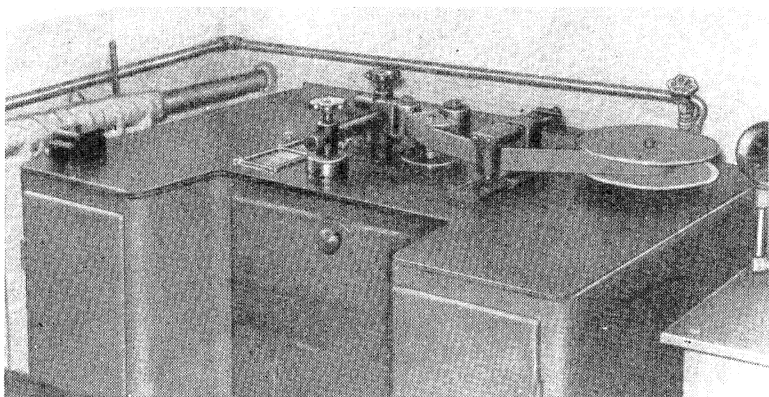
Станок для навивки ленточных сердечников из холоднокатаной стали
